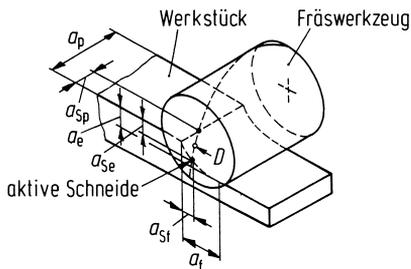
Eingriffsgrößen des Werkzeuges und der Schneide beim Umfangsplanfräsen (nach DIN 6580)
